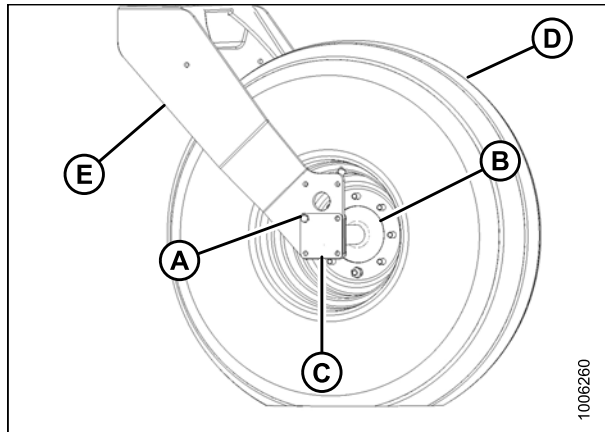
Самоустанавливающееся колесо в сборе
